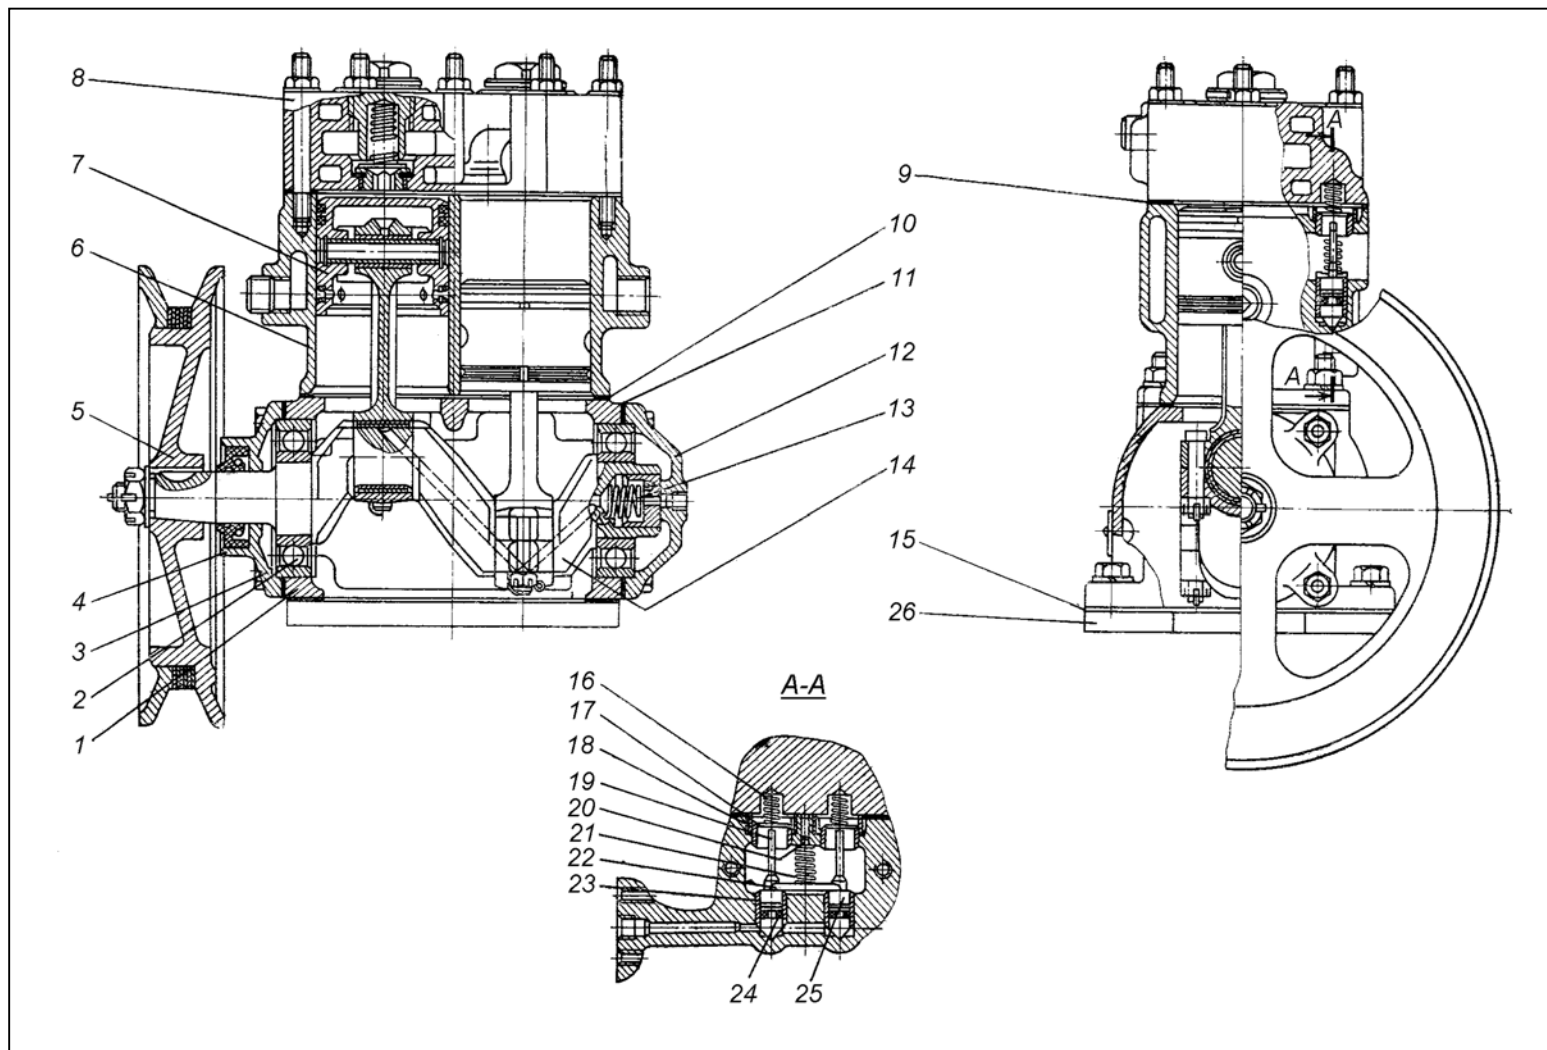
Компрессор пневматического тормоза в сборе: 1- картер компрессора в сборе; 2 – подшипник 207; 3 – передняя крышка компрессора; 4 – сальник в сборе; 5 – шкив компрессора; 6 – блок цилиндров; 7 – поршень с шатуном; 8 – головка цилиндров; 9 – прокладка головки; 10 – прокладка блока цилиндров; 11 – прокладка крышки картера; 12 – задняя крышка картера компрессора; 13 – пружина уплотнительная; 14 – коленчатый вал; 15 – прокладка нижней крышки; 16 – пружина нагнетательного клапана; 17 – клапан впускной; 18 – направляющая впускного клапана; 19 – шток впускного клапана; 20 – направляющая пружины коромысла; 21 – пружина коромысла; 22 – коромысло впускных клапанов; 23 – плунжер; 24 – кольцо уплотнительное; 25 – гнездо штока впускного клапана; 26 – нижняя крышка.
